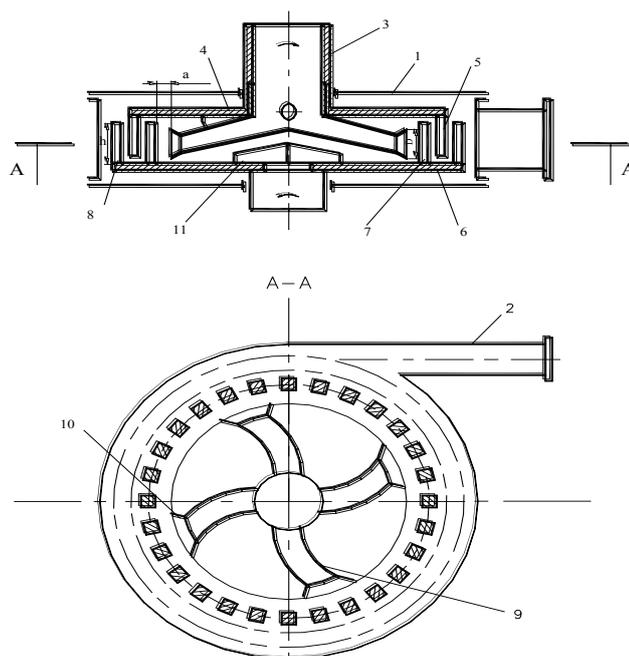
Дезинтегратор с наклонно установленными цилиндрическими разбрасывающими патрубками
